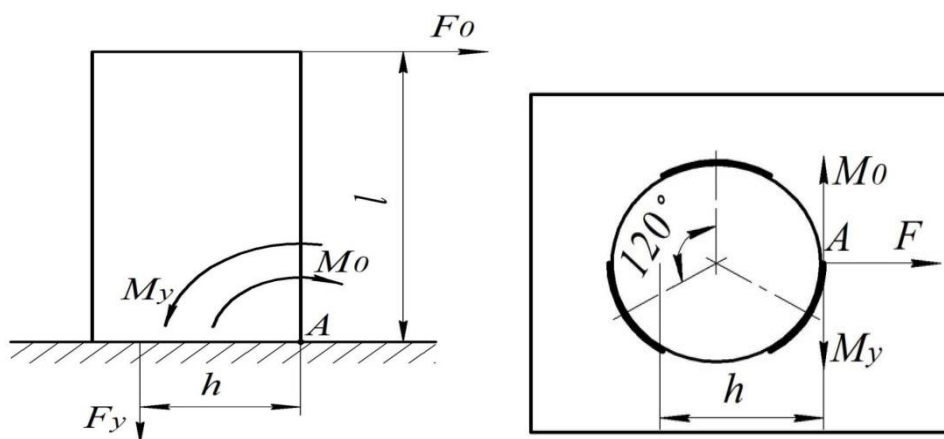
Схема равномерного трехпозиционного расположения сварных швов соединения
